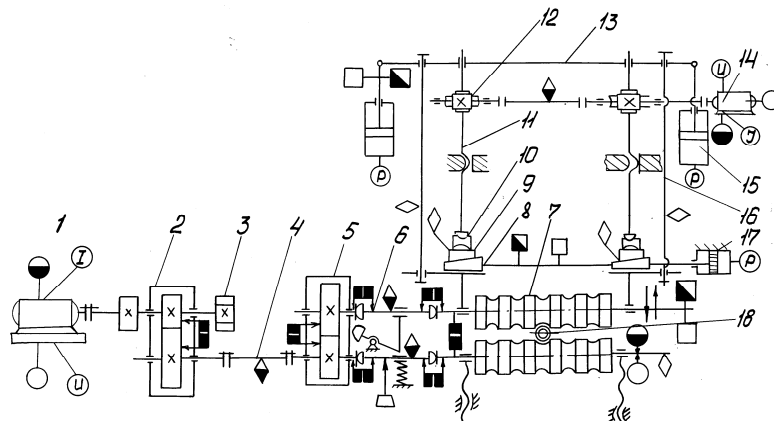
Кинематическая схема главного привода автоматического стана трубопрокатного агрегата
